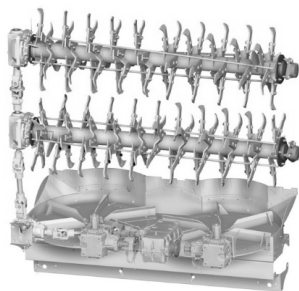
Фрезерный агрегат с центробежными дисками разбрасывателя модели FERTI-SPACE 2 фирмы «JOSKIN»
